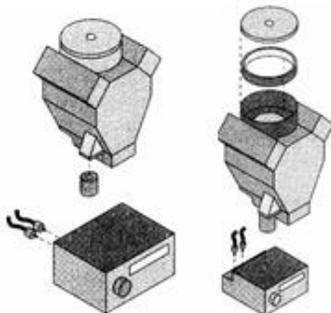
Diseñe la pieza base de dimensiones grandes, después, inserte las piezas pequeñas subsecuentes con ensamble piramidal sobre un solo eje.
